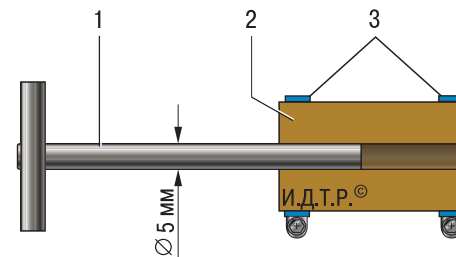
Приспособление для притирки клапанов: 1 – металлический стержень; 2 – резиновый шланг; 3 – винтовые хомуты
